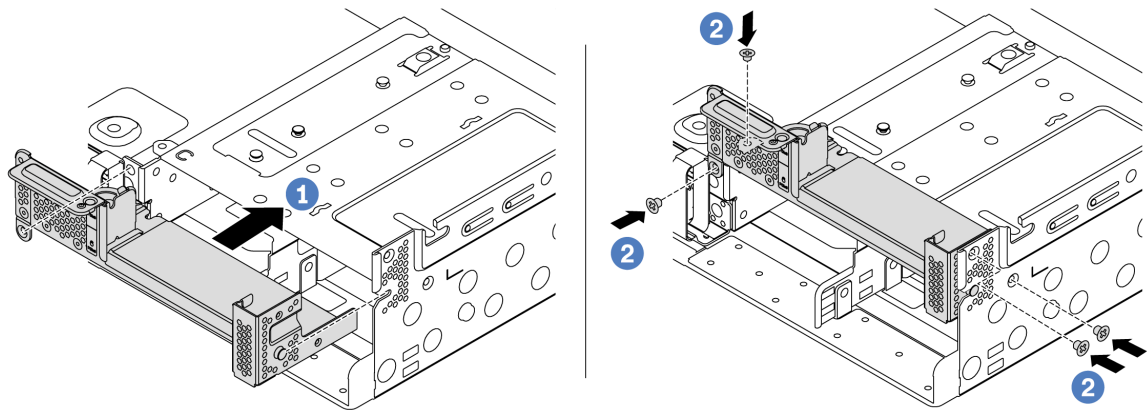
Installazione della staffa posteriore C1 per il montaggio a parete
